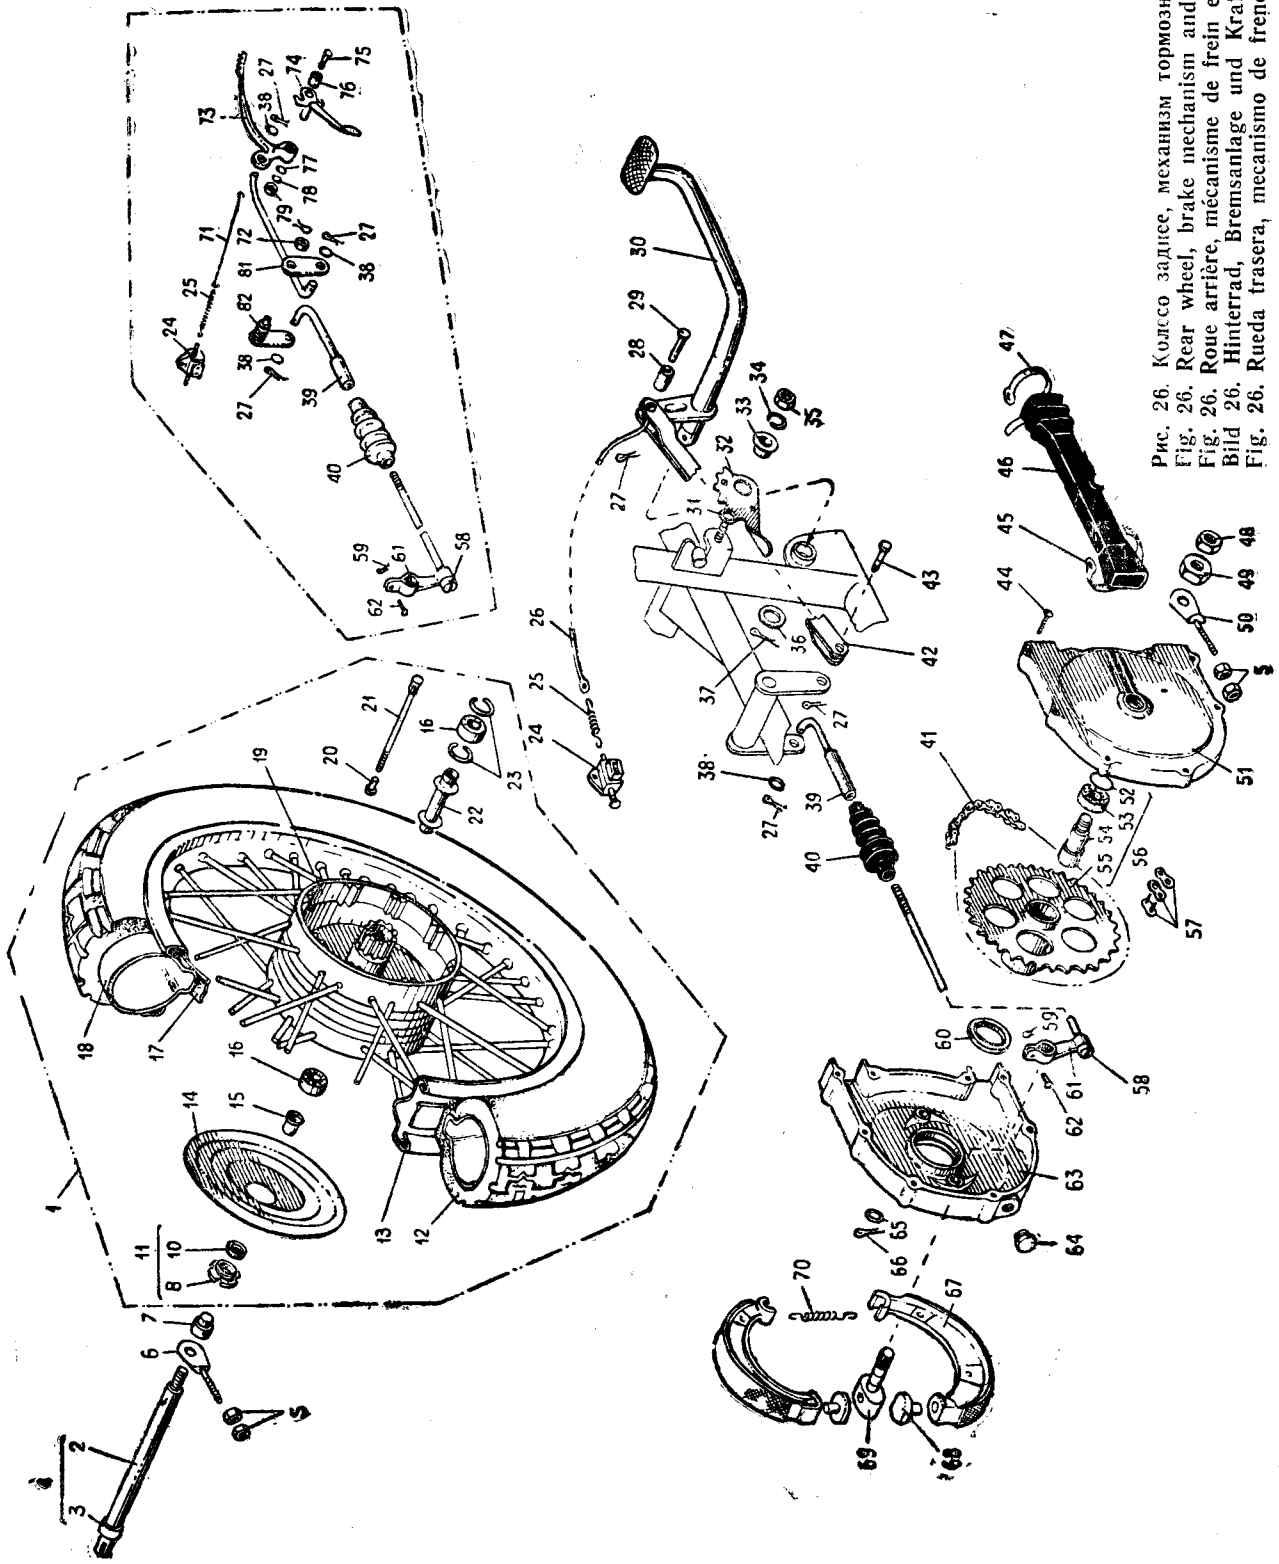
Колесо заднее, механизм тормозной и передача силовая В.1.10
